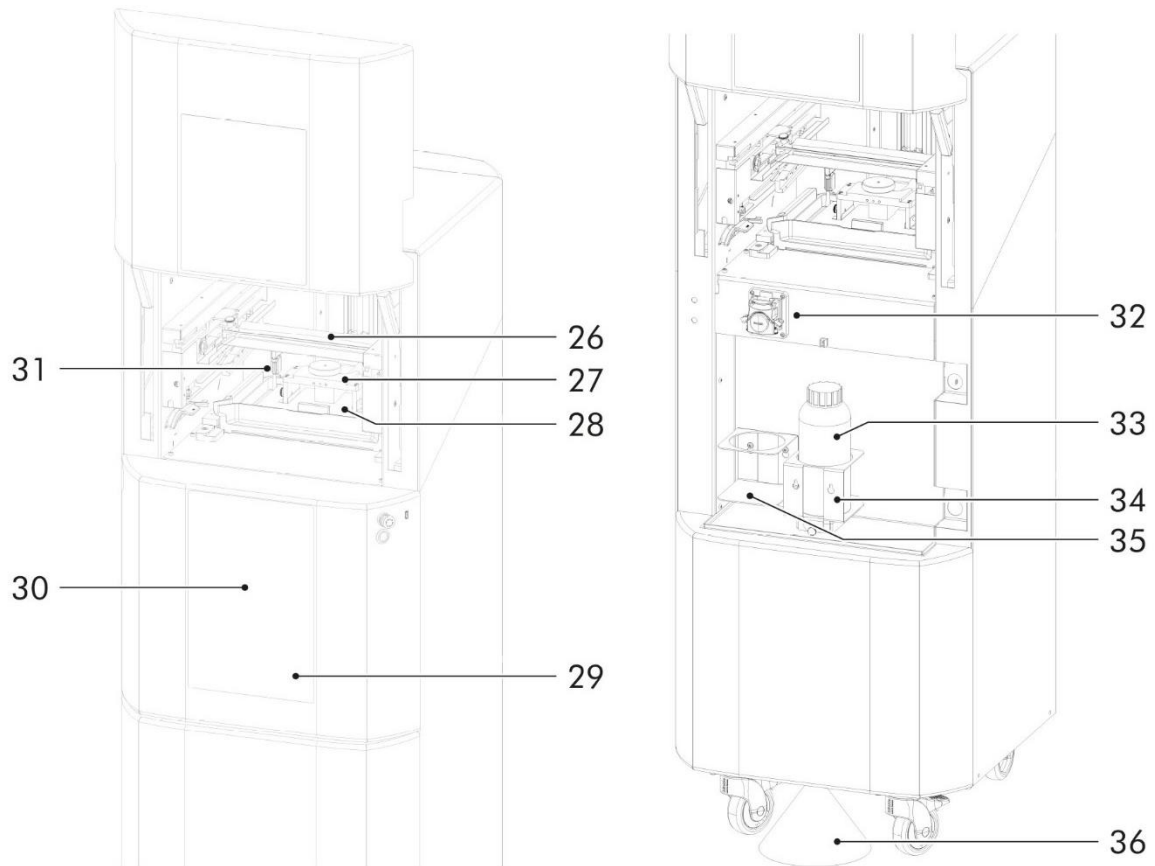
Aperçu de la machine, espace de fabrication & capot intermédiaire
